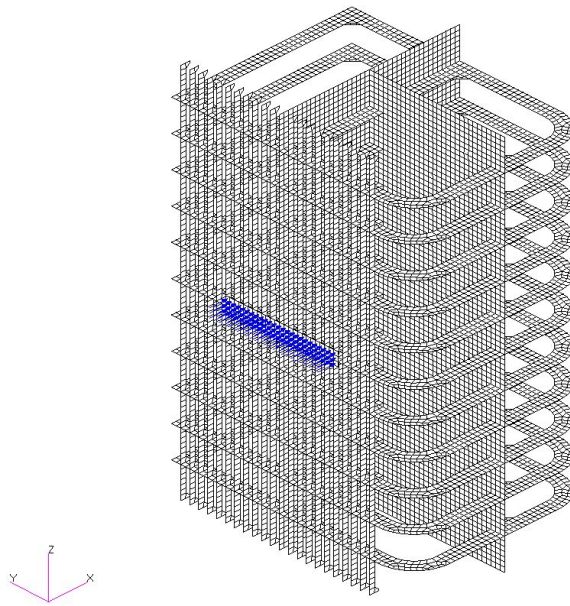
하중조건 1의 빙하중 형상 및 위치
